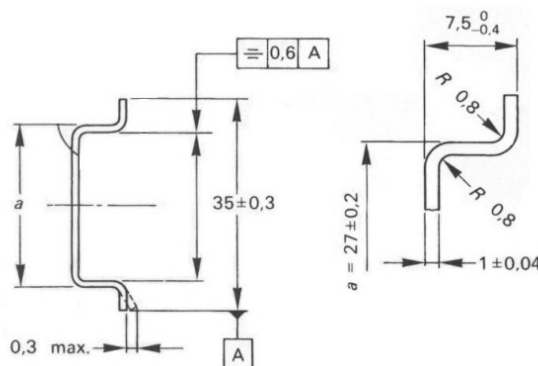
Dimensões (mm) das calhas metálicas de perfil normalizado do tipo TH 35-7.5
